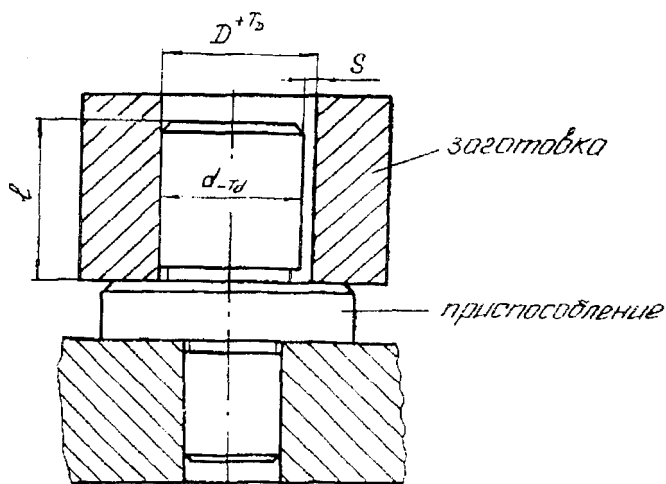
Схема базирования заготовки на цилиндрический палец
